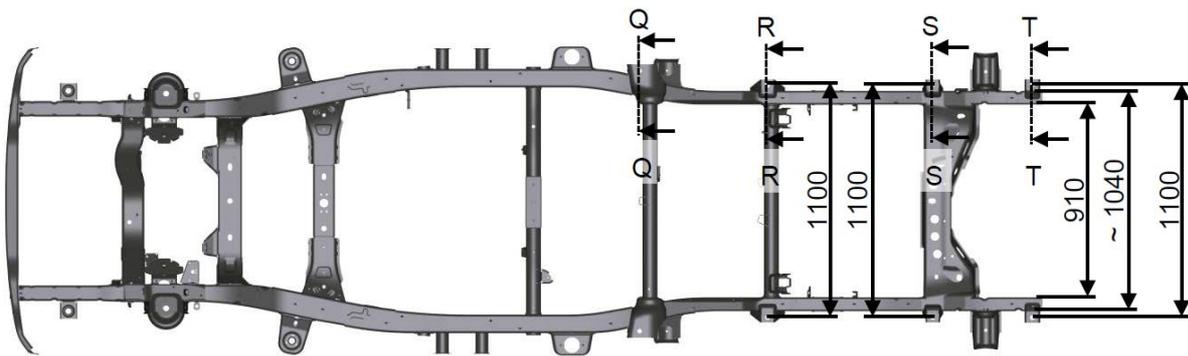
Vista de planta del bastidor Amarok SC
